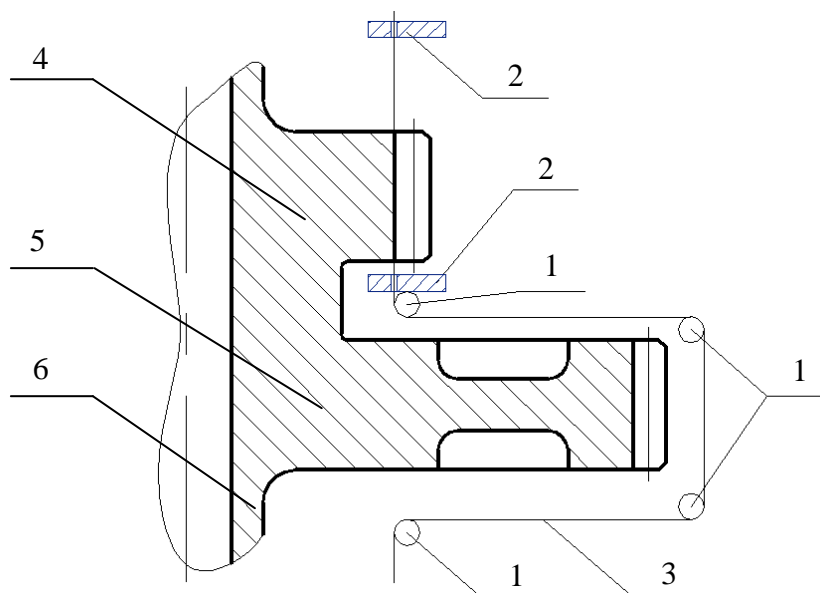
Схема ЭЭО цилиндрического эвольвентного закрытого венца цельного блока зубчатого колеса: 1 – ролики; 2 – алмазная направляющая; 3 – проволока; 4 – закрытый венец; 5 – открытый венец; 6 – цельный блок зубчатых колес
